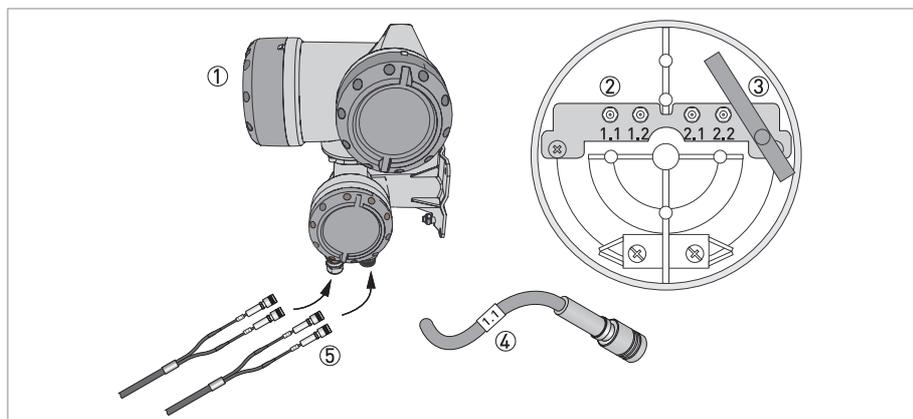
Conexão do cabo de sinal ao conversor de sinal
